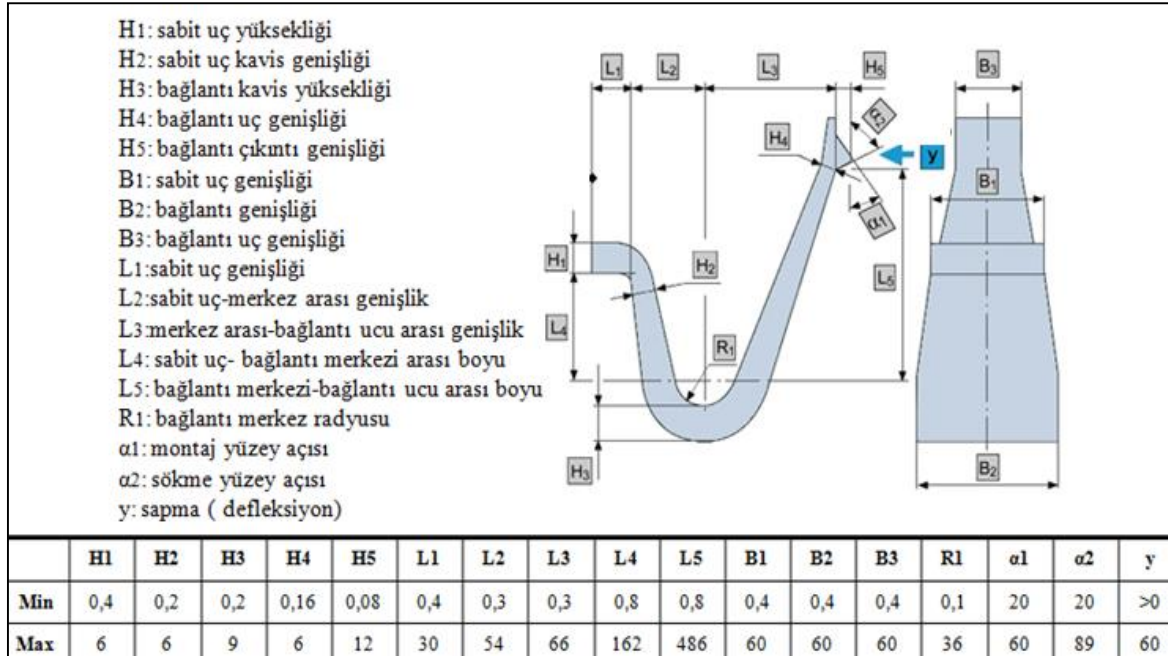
S tipi esneyerek kilitlenen bağlantı elemanının boyutlandırılması [42]
